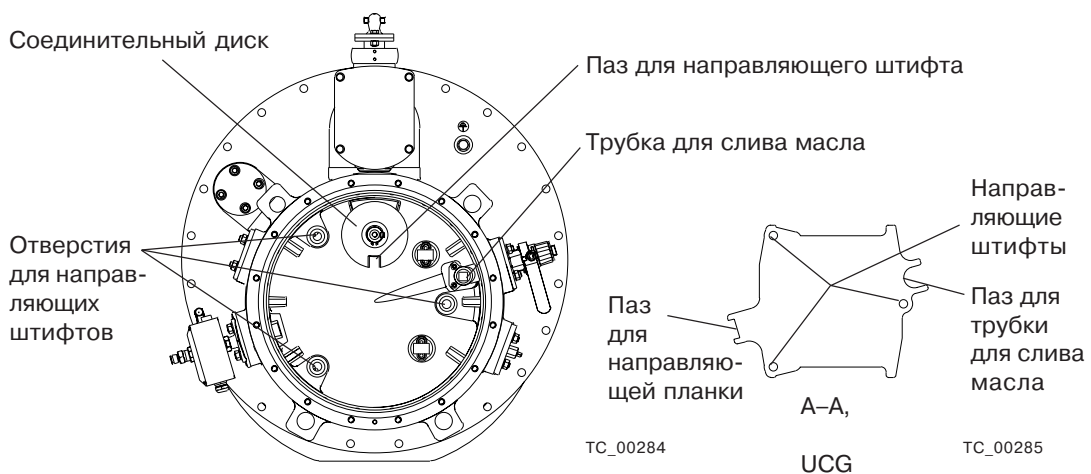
UCG Корпус дивертерного переключателя, вид сверху
